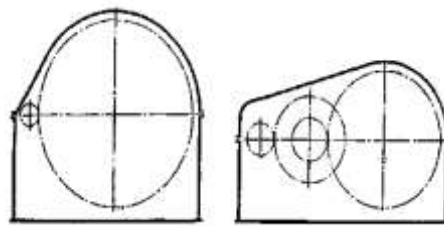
Сопоставление габаритов одноступенчатого и двухступенчатого редукторов с цилиндрическими колесами при одинаковом передаточном числе $u = 8,5$
